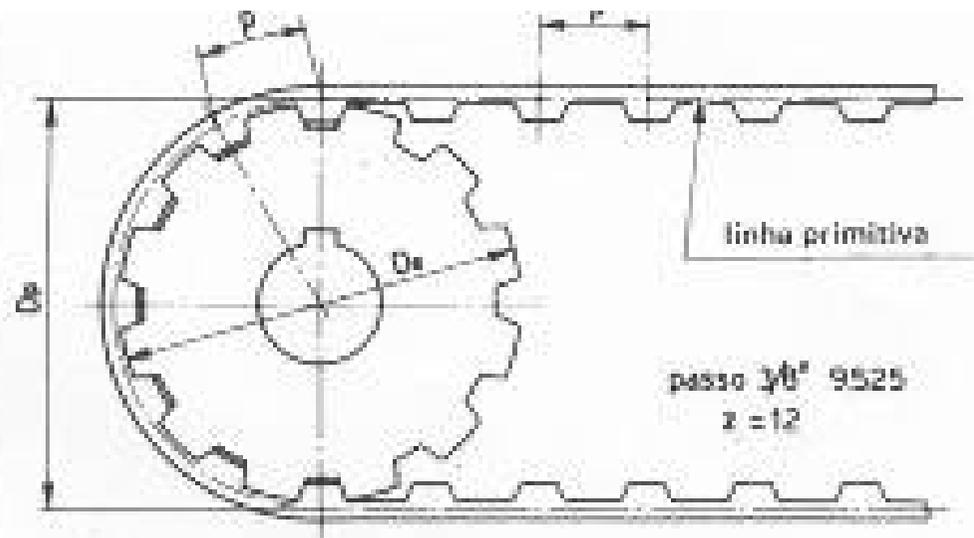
Exemplo de transmissão mediante correia dentada: a linha primitiva coincide com o eixo do inserto.
